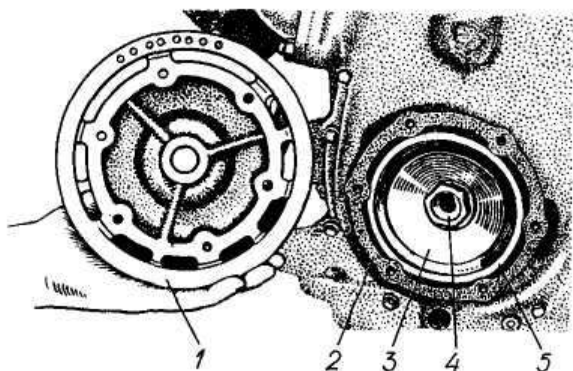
Центробежный маслоочиститель со снятой крышкой:
